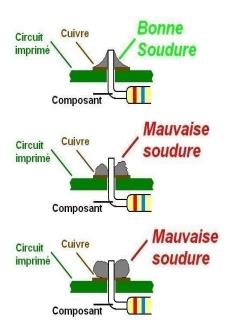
Exemple de bonne et mauvaise soudure
